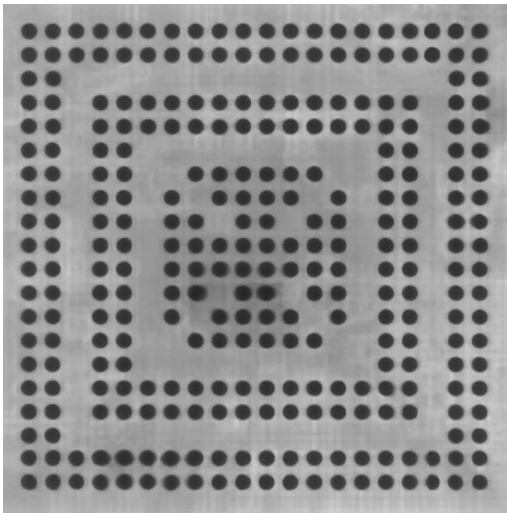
3D-Schichtbild des BGA (obere Bestückseite)
